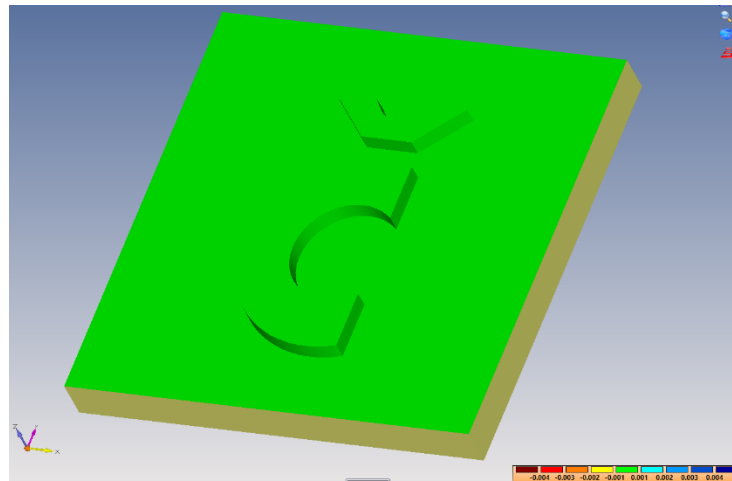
Náhled drah frézování na čisto frézou T50
